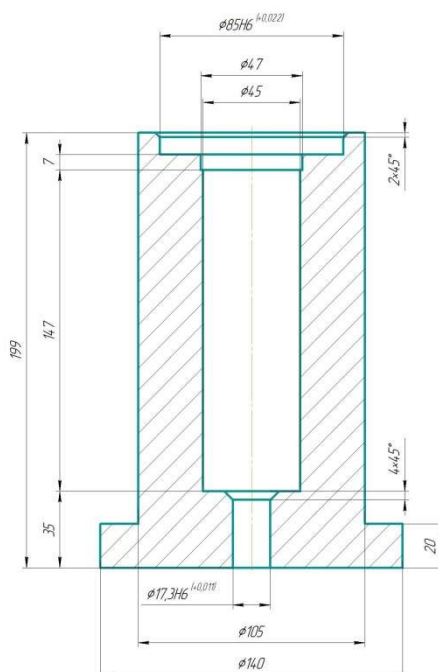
Центрирующее приспособление для сборки клеевого соединения «ведущий вал-подшипник» коробки передач автомобиля ГАЗ-53
